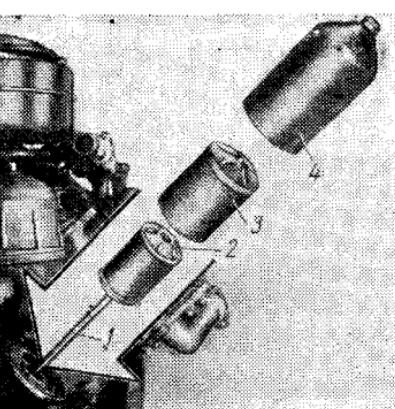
Порядок разборки фильтра грубой очистки масла:
